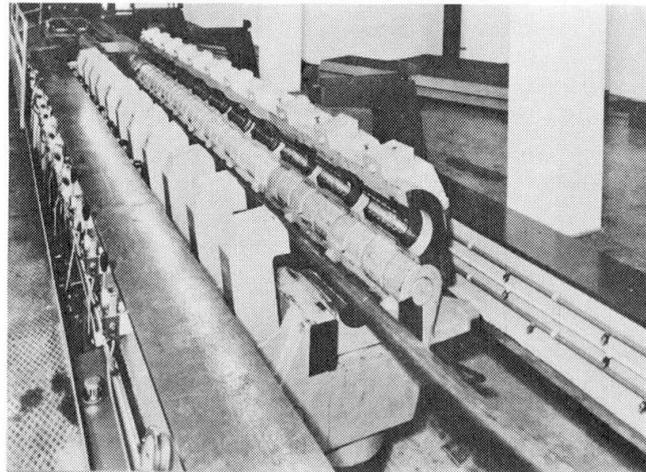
Klemmenwagen mit elf hydraulisch betätigbaren Klemmbacken
